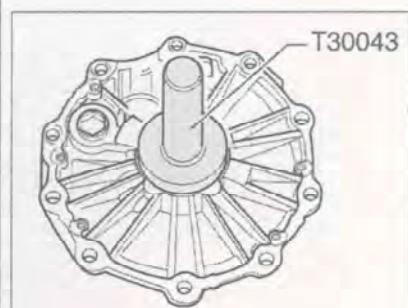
С помощью приспособления T30043 установите новый сальник левого вала на глубину 5.5 мм в крышку главной передачи.
